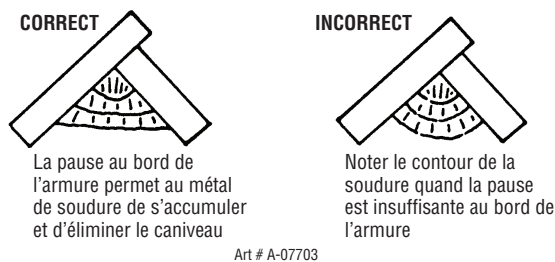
Exemples de soudures de joint vertical
